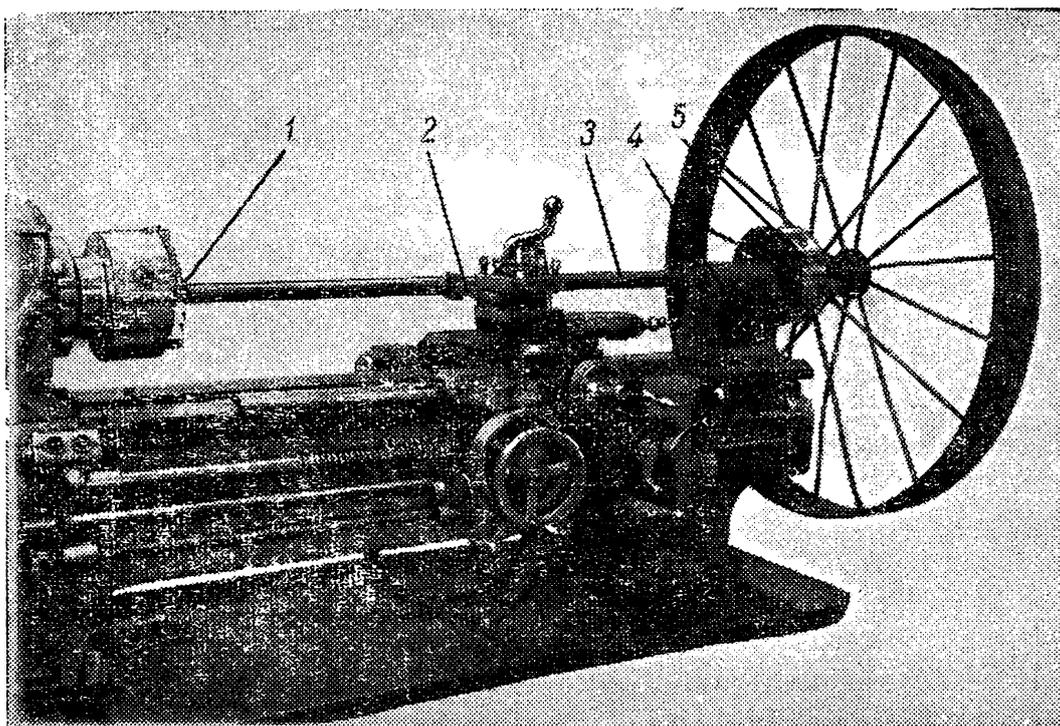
Приспособление для расточки ступиц колес сельскохозяйственных машин:
